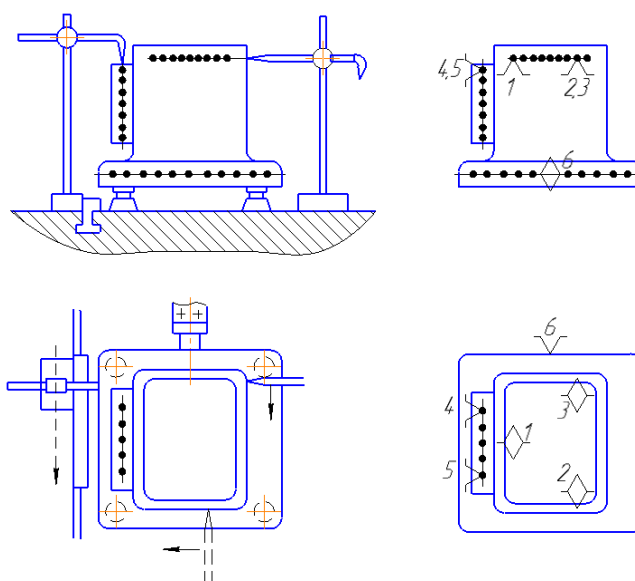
Установка на станке заготовки корпусной детали с выверкой ее положения по разметочным рискам: 1–6 – опорные точки
